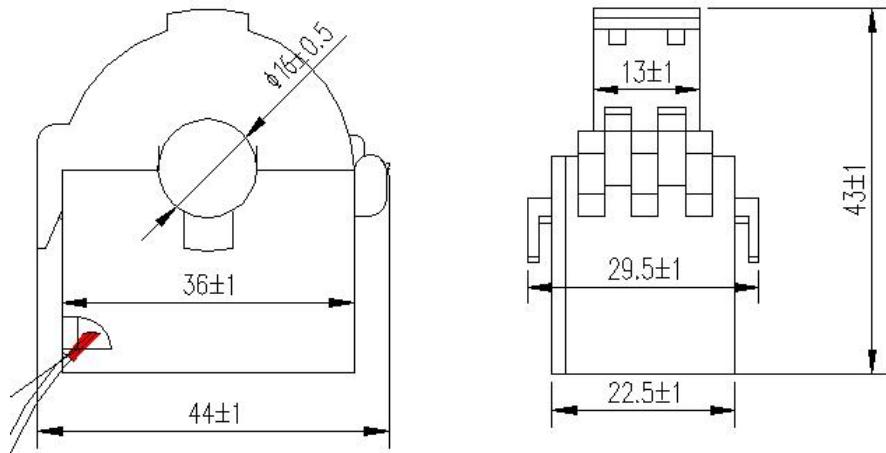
ADW300W 配套互感器 HCT16K-FJ 尺寸图
